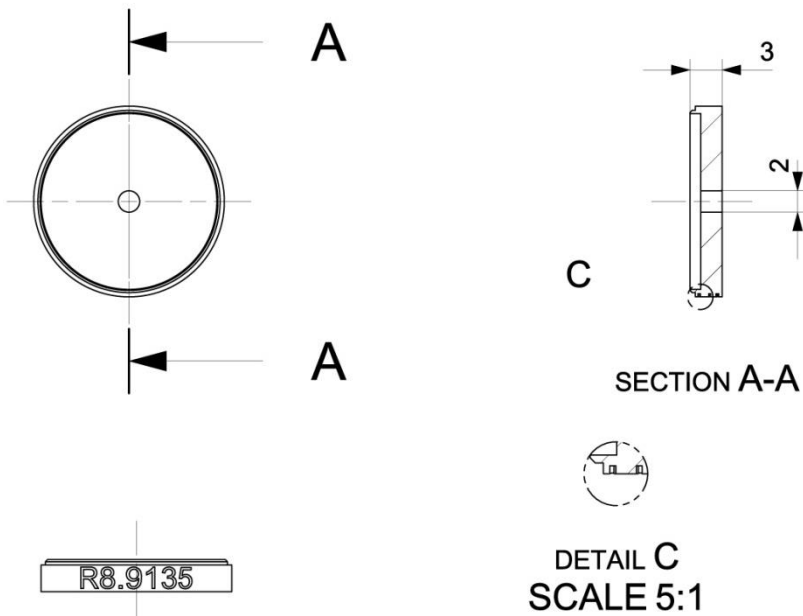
Technische Zeichnung Kappchen für Aktormodulgehäuse V02T18
